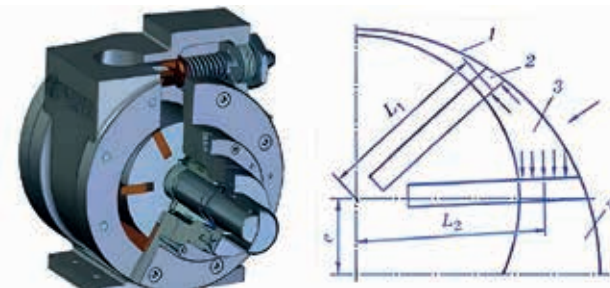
Пластинчастий гідромотор і схема його роботи: 1 – статор; 2 – пластина; 3 – робоча камера; 4 – ротор; e – ексцентриситет; L_1 і L_2 – плечі дії рівнодійної сили тиску рідини
